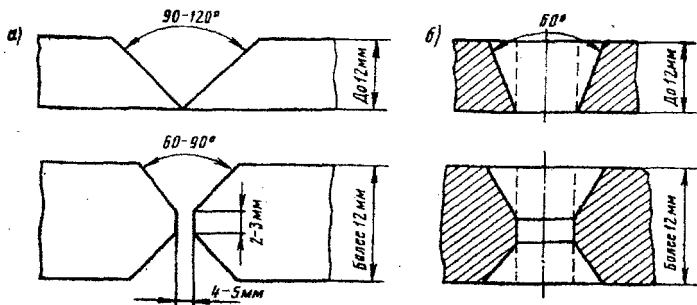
Подготовка трещины (а) и отверстия (б) к заварке.
